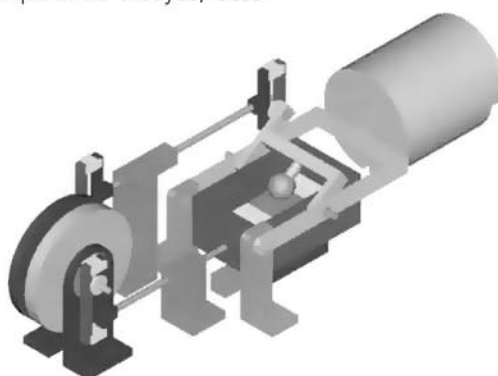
Esquema de máquina de ensayos desarrollada mediante técnicas CAD.
